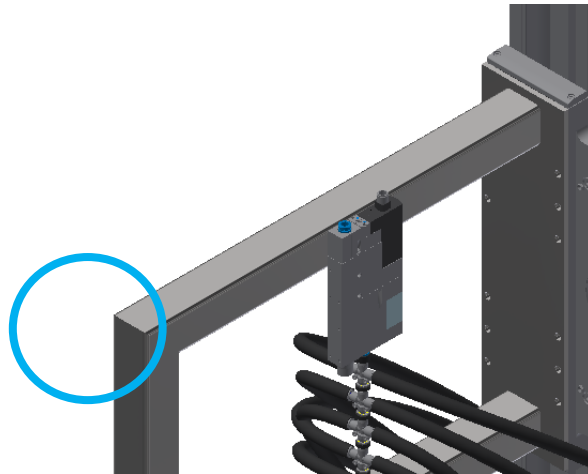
26. Sección crítica para análisis de soldadura.
